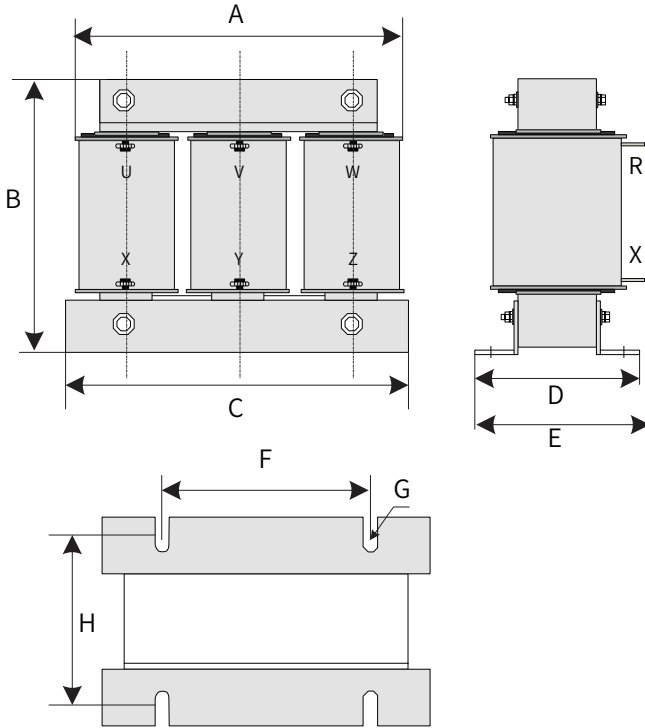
Размеры выходного реактора переменного тока 30 - 60 А
